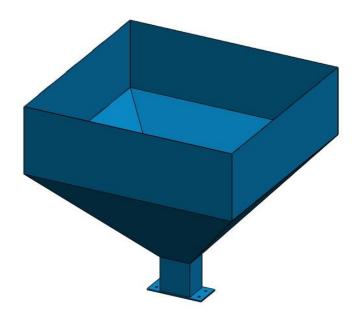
Tolva de almacenamiento diseñada en programa CAD Solidworks, C. Jiménez.
